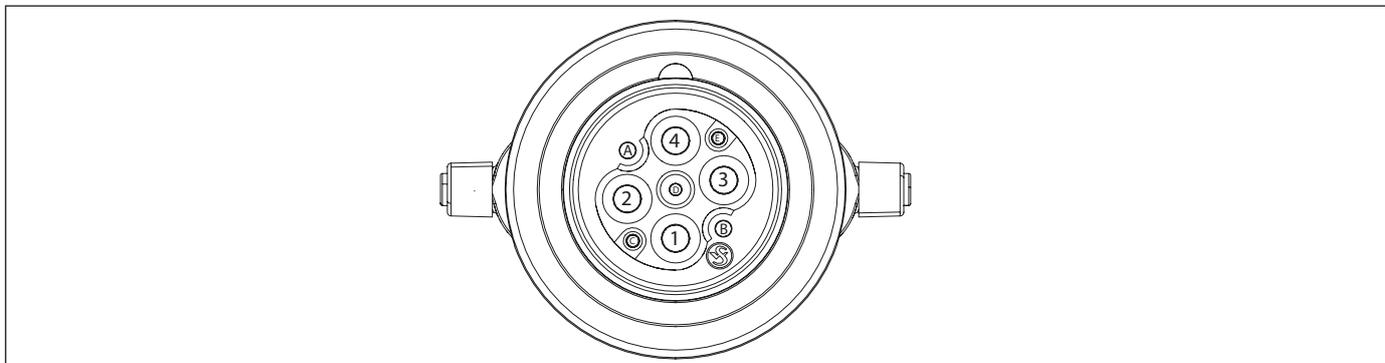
Kennzeichnung der Buchsenkontakte am Stecker
